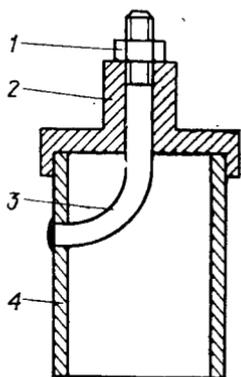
Приварка шпильки к корпусу колпачка:
